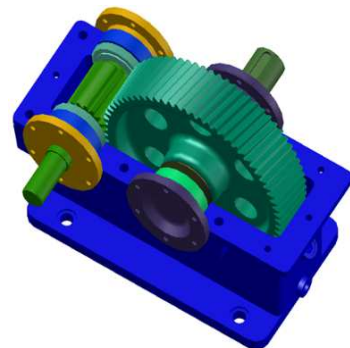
3D модель циліндричного одноступеневого косозубого редуктора, виконана в AutoCAD
